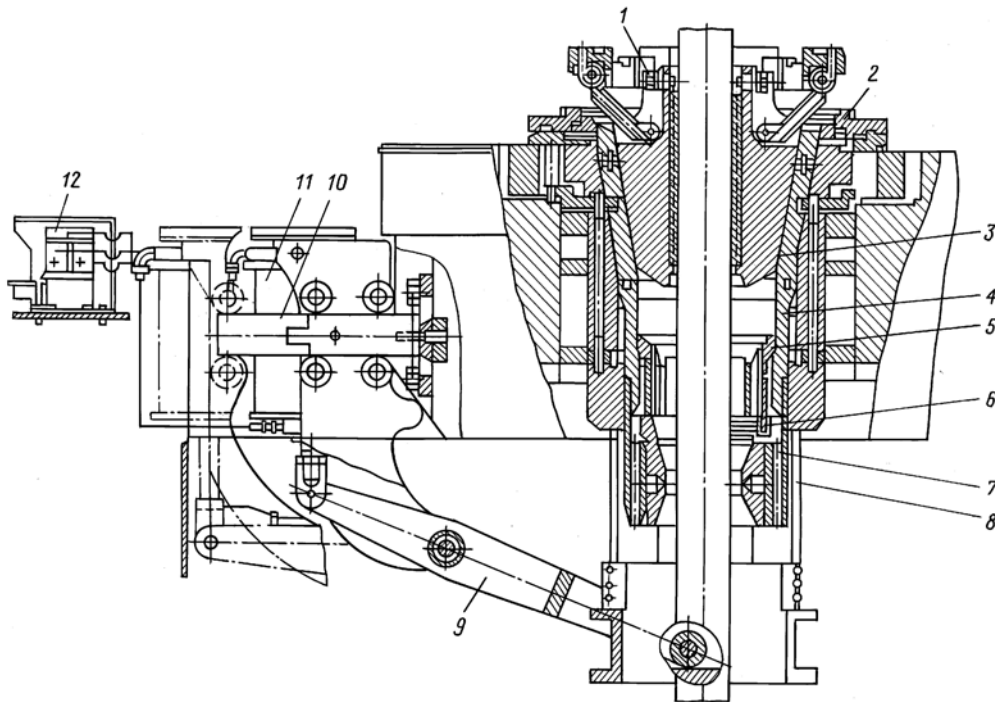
Пневматический клиновой захват ПКРО-560М:
